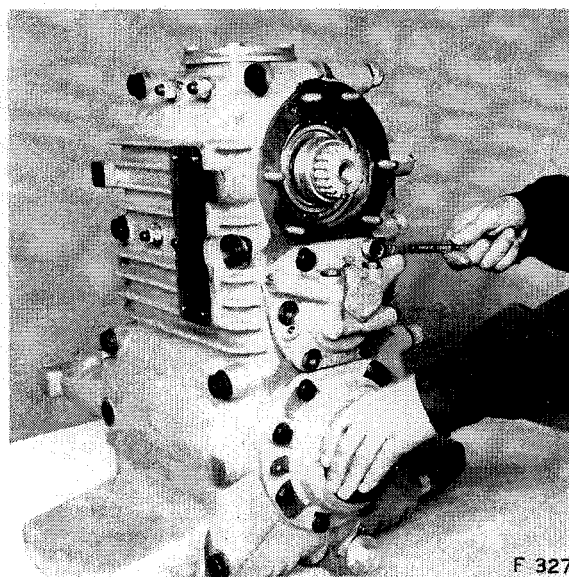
Lösen der Befestigungsschrauben der Zwischenwellen-Lagergehäuse
